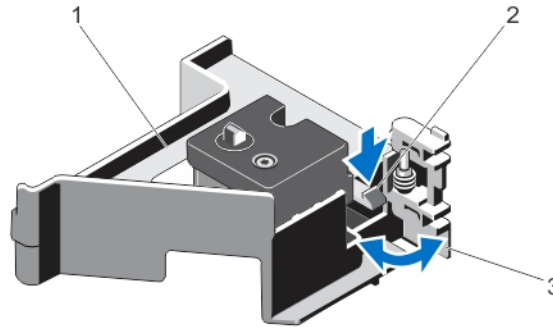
Ouverture et fermeture du loquet du support de carte PCIe
